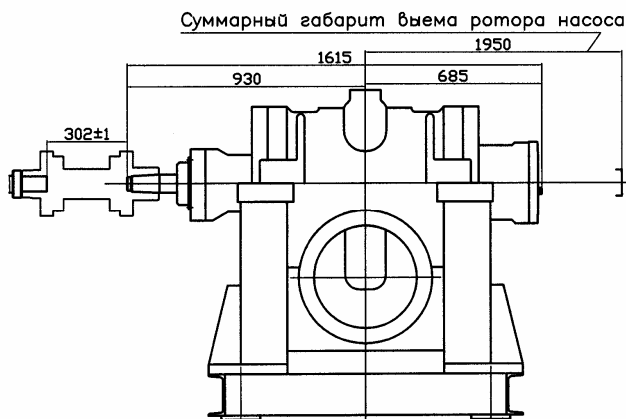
Общий вид насоса аварийного расхолаживания ЦНР 800-230/1.
